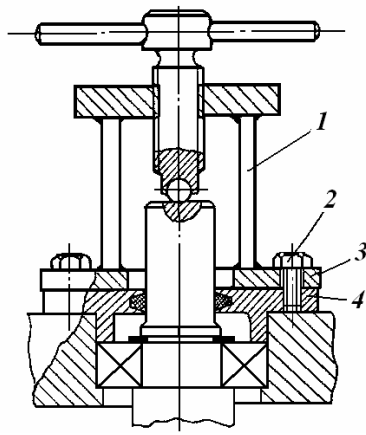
Винтовой съемник, закрепленный на снимаемой детали:
